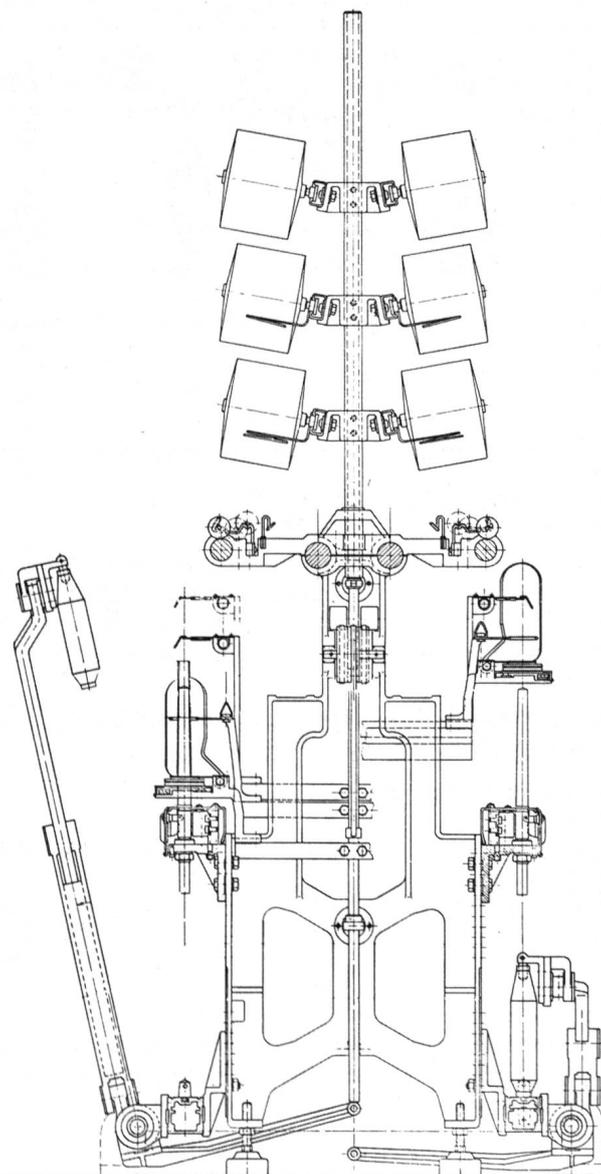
Querschnitt Ringzwirnmaschine «Zinser»
